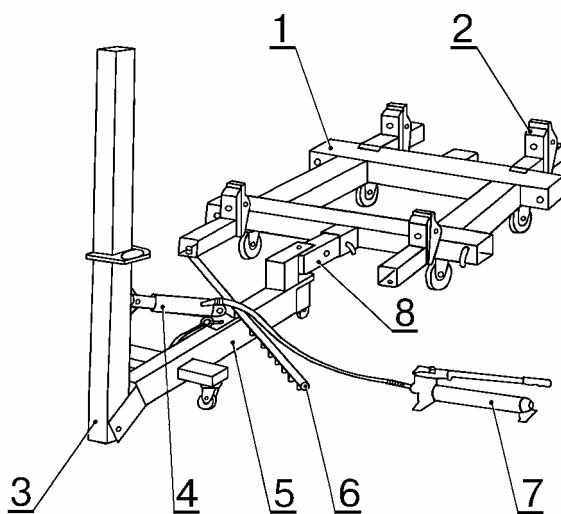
Общий вид универсального станда для правки кузовов легковых автомобилей (миниробот), модель 67.21.015:
